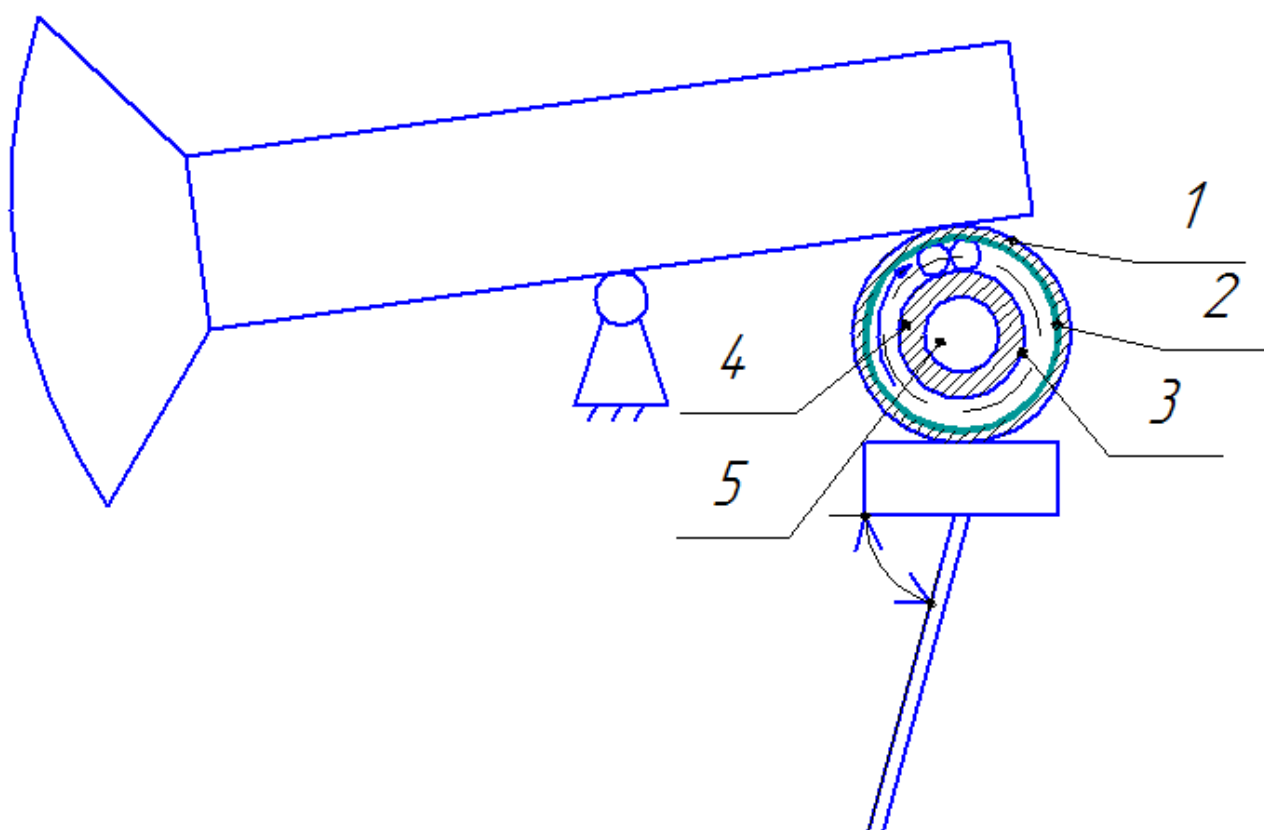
Схема подшипниковой опоры траверсы с храповым механизмом
